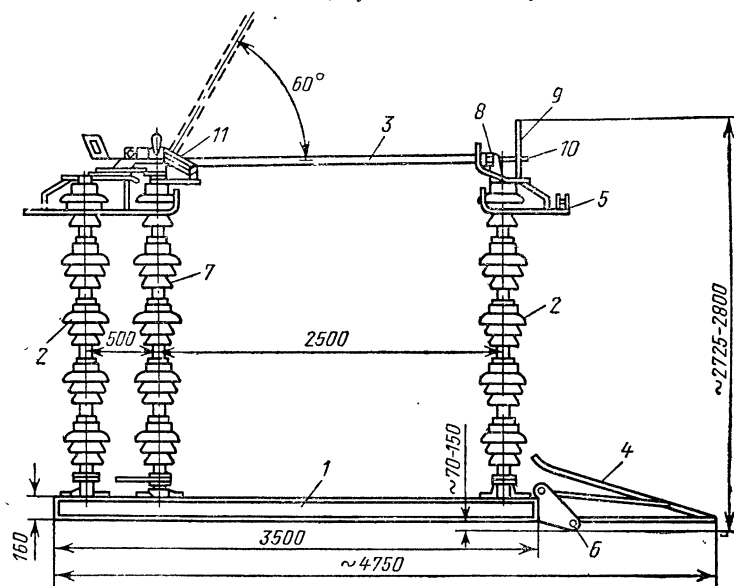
Разъединитель наружной установки рубящего типа с заземляющим ножом, $U_n=220$ кВ.
